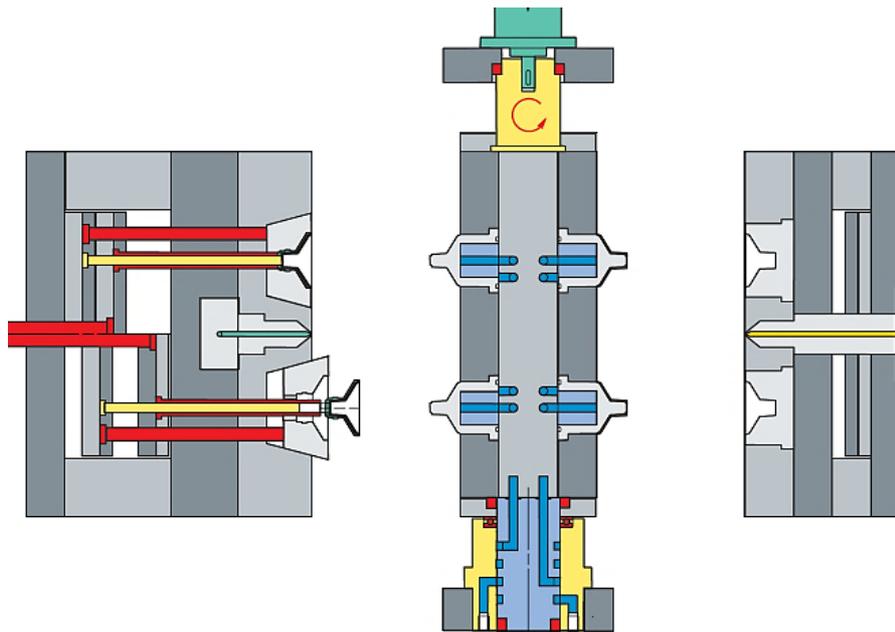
Molde bimaterial - rotação vertical da placa do molde. [14]
